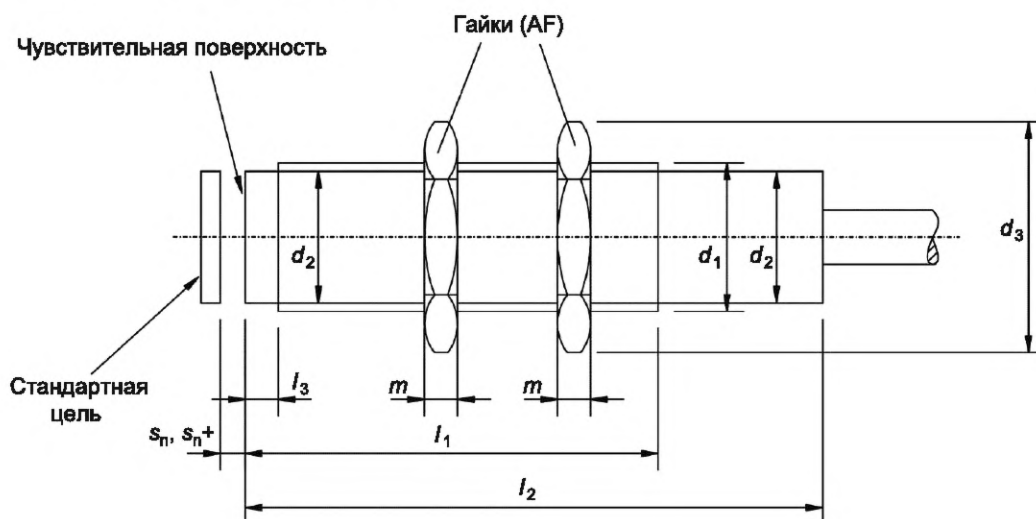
(IA) Габаритные размеры с резьбой на корпусе. Тип кабеля
